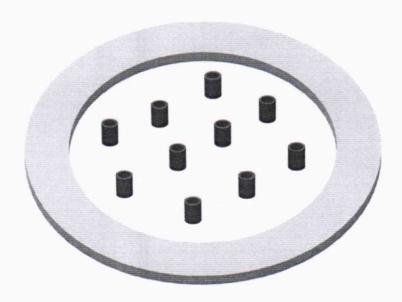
Схема установки алюминиевых втулок внутри вспомогательного кольца
